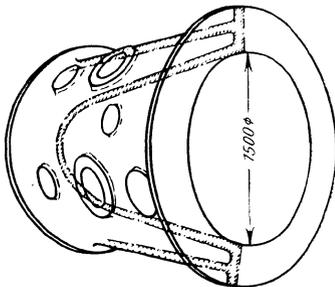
Kochbottich mit Arbeitsflächen für Armaturen.
